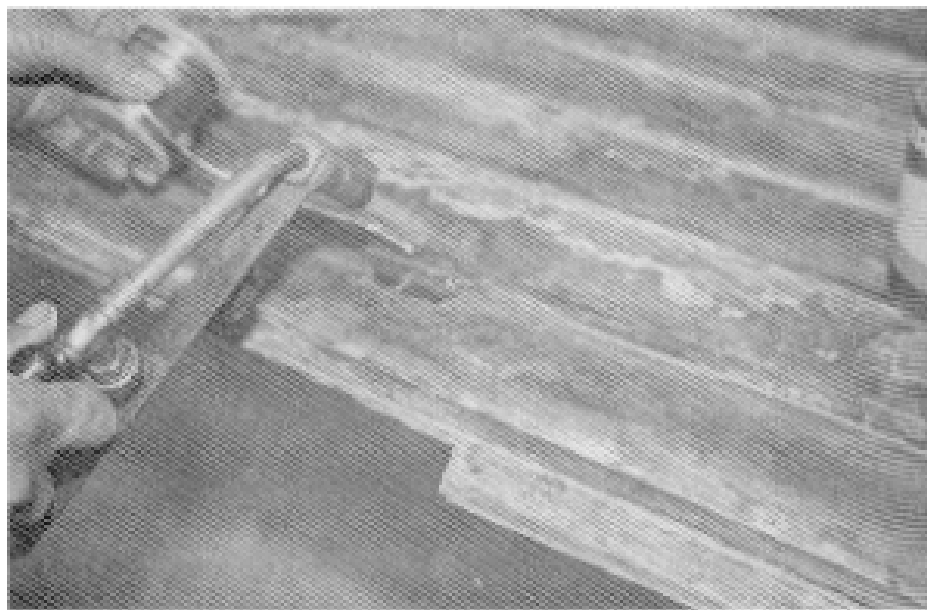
Lámina de cobre soldada al tubo de 0.95 cm (3/8 pulg.) de
